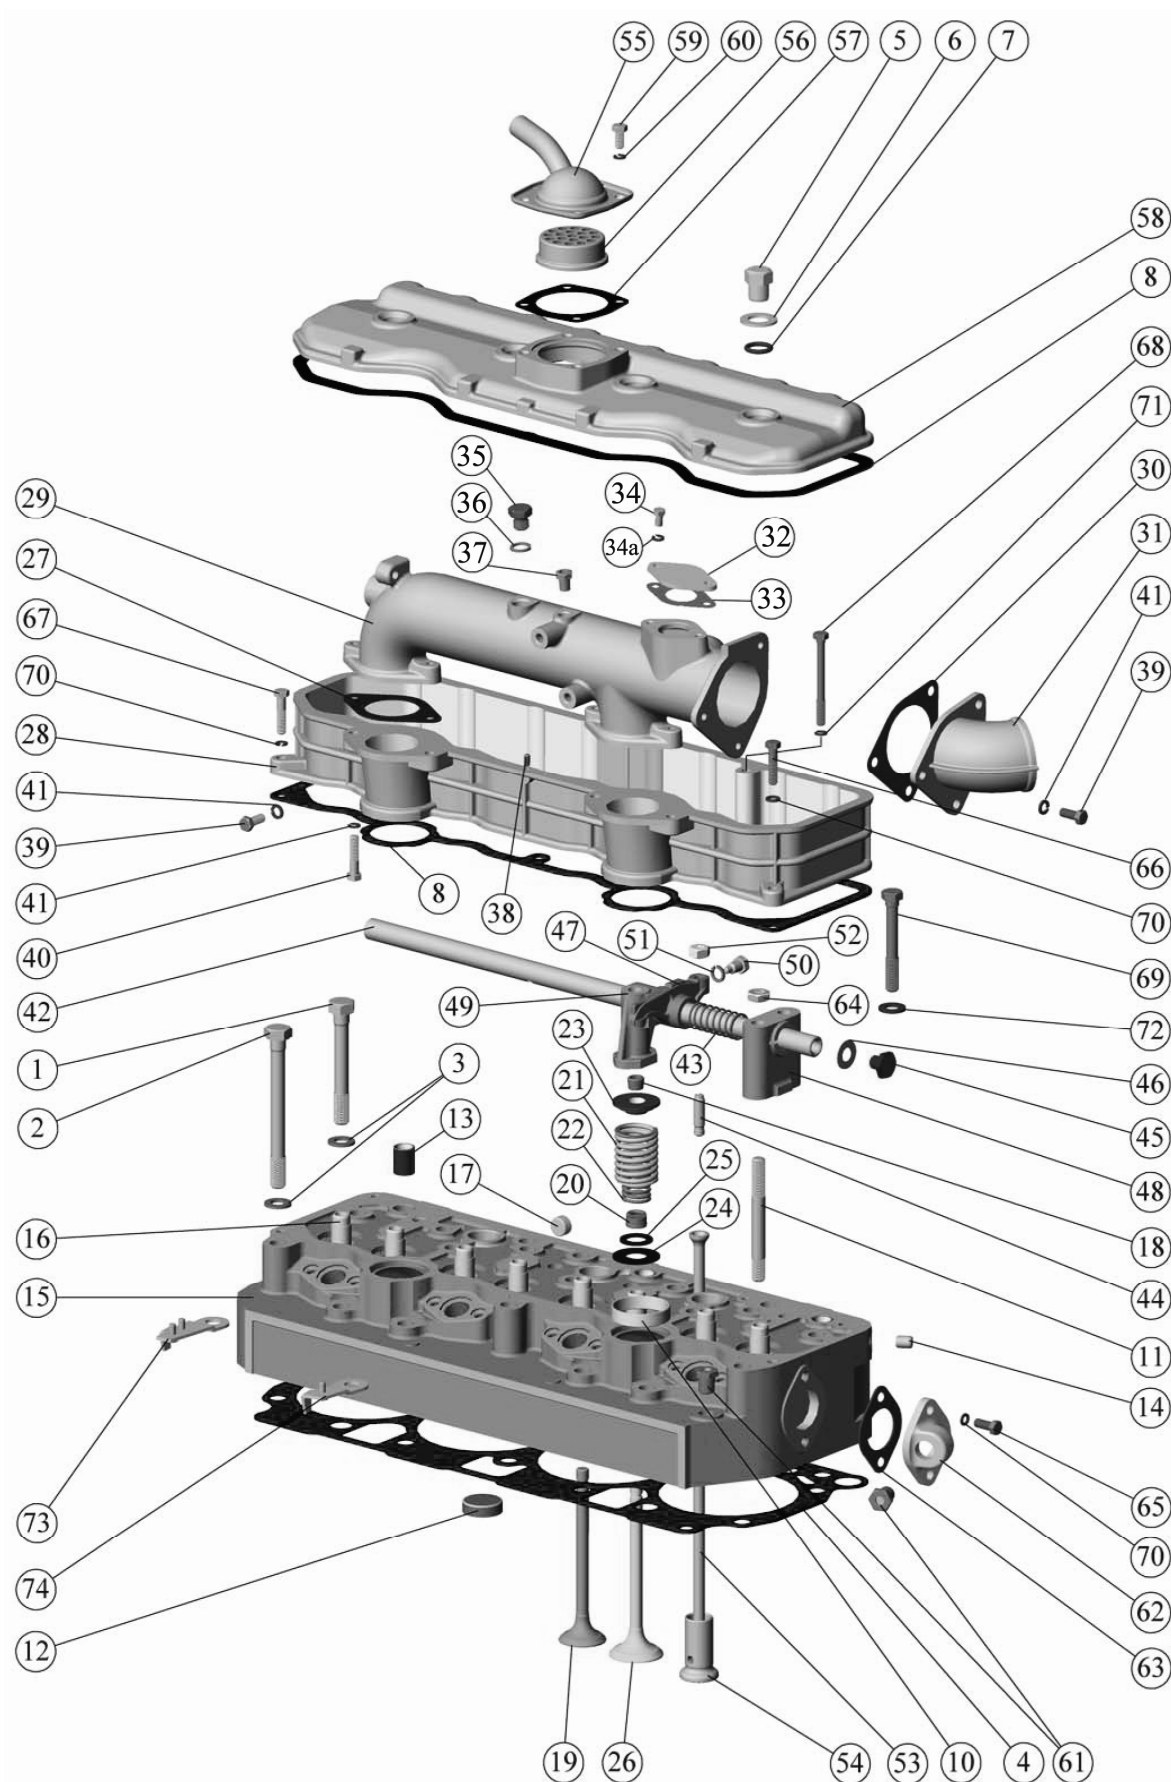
Установка головки цилиндров и впускного тракта (для двигателей Д-244)
